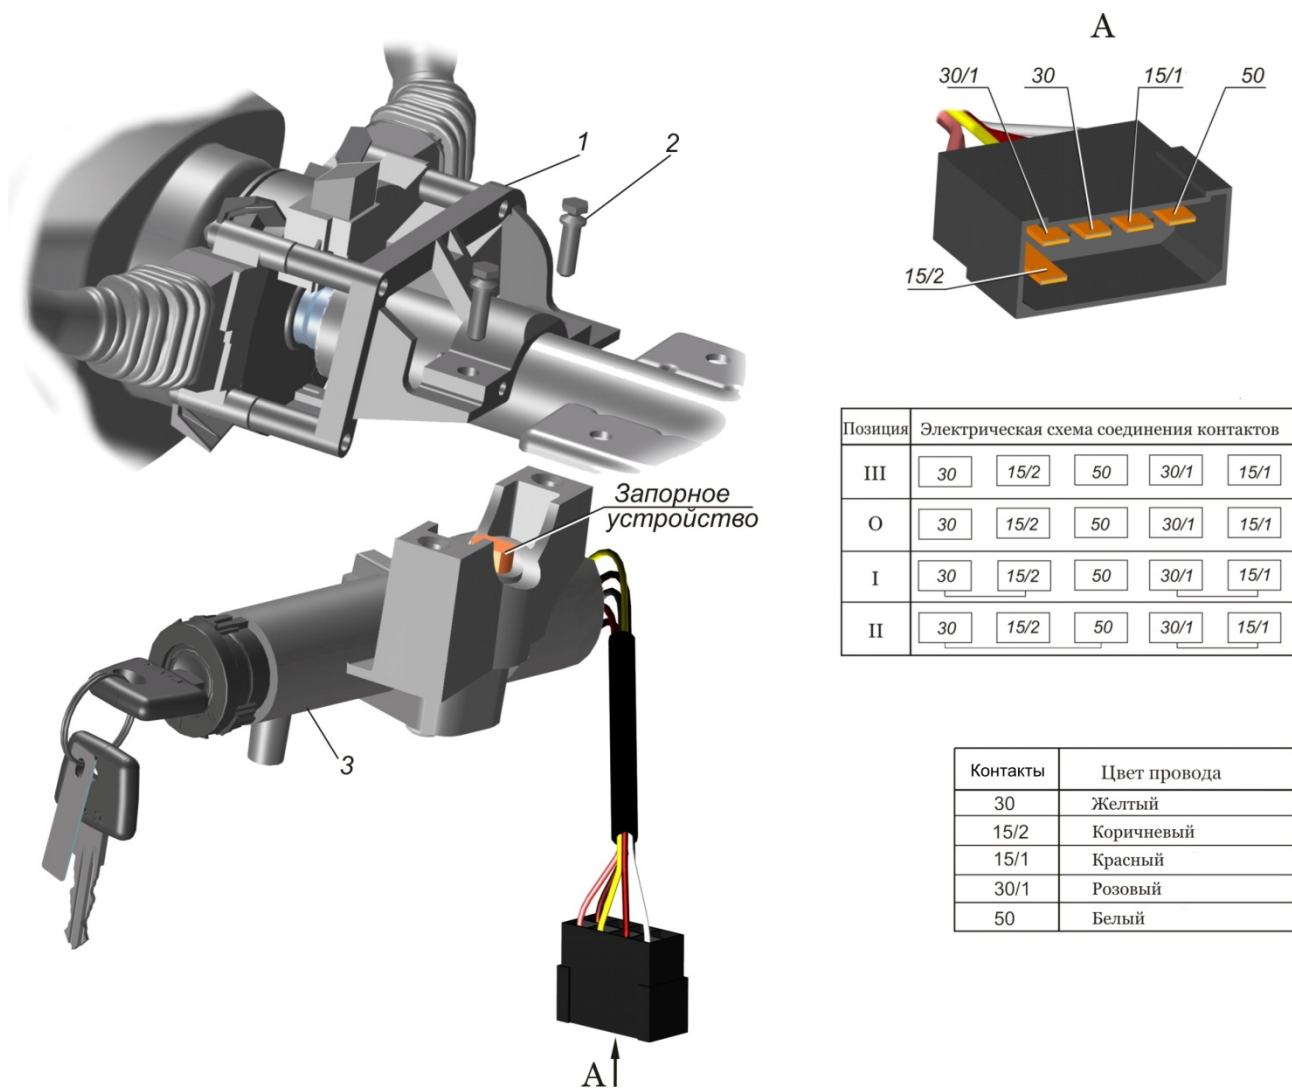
Установка выключателя приборов и стартера 3111.3704010-20: 1 – рулевая колонка; 2 – болт; 3 – выключатель приборов и стартера
